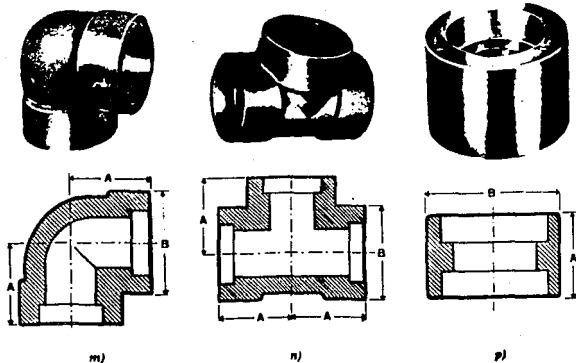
m) Codo de 90° para soldar a enchufe. n) Te para soldar a enchufe. p) Manguito de unión para soldar a enchufe.
